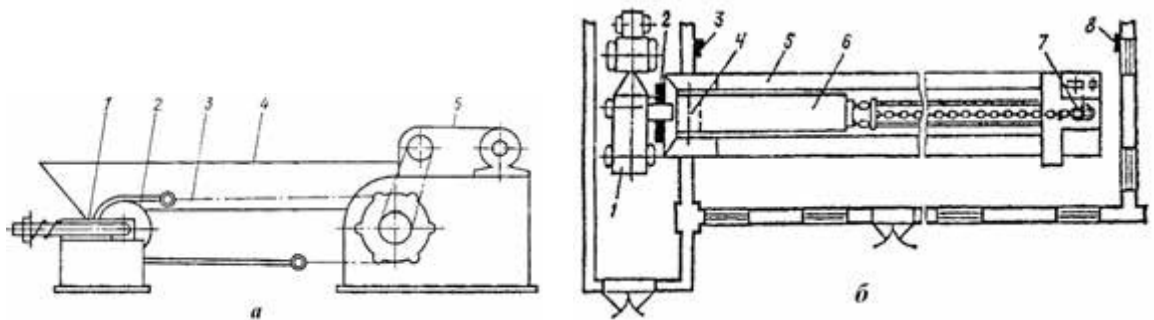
Стрічковий роздавач кормів: а – конструктивно-функціональна схема: 1 – натяжна станція; 2 – ведений барабан; 3 – робочий орган; 4 – годівниця; 5 – приводна станція; б – план розміщення обладнання та конструкція робочого органа: 1 – мобільний кормороздавач; 2 – приямок; 3, 8 – лінійні вимикачі; 4 – натяжна станція; 5 – кормовий жолоб; 6 – робочий орган; 7 – приводна станція;
